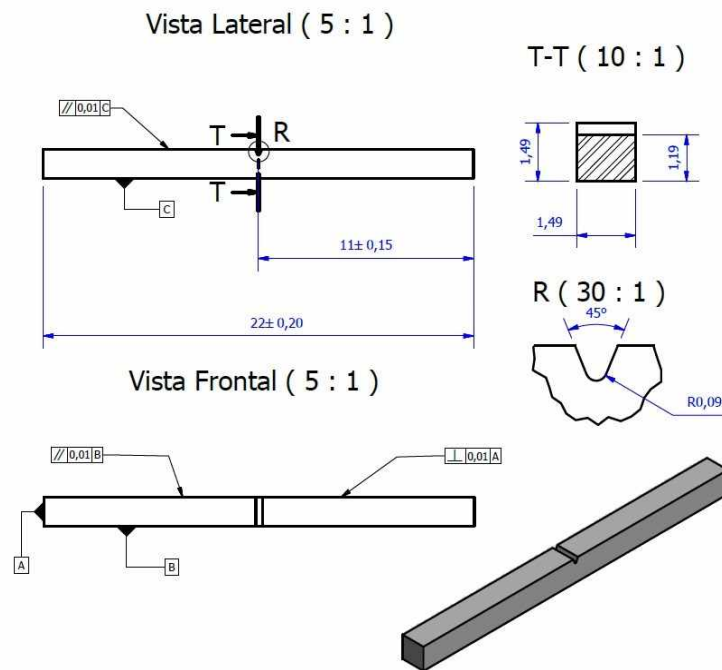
Corpo de prova secção 1,49 mm x 1,49 mm, raio 0,09 mm.
